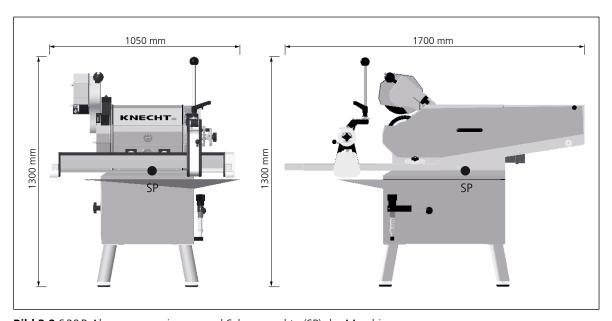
S20B Abmessungen in mm und Schwerpunkte (SP) der Maschine
